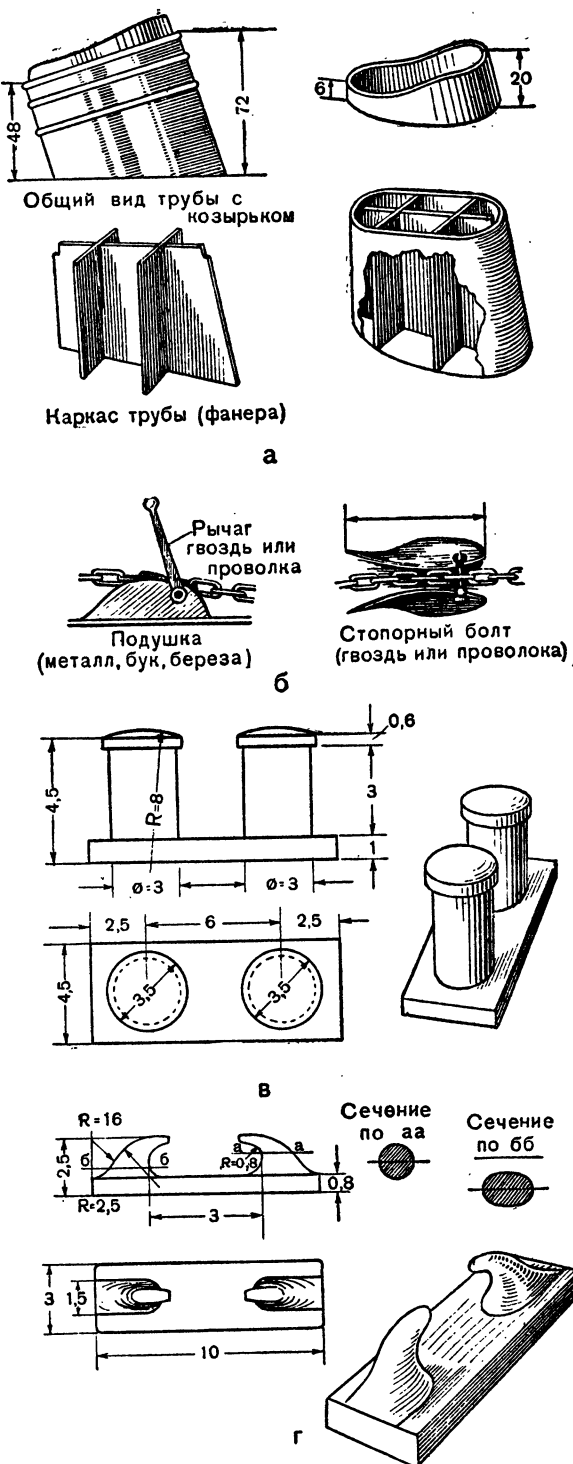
Надстройки кораблей: труба, стопор якоря, кнехт и киповая планка.
